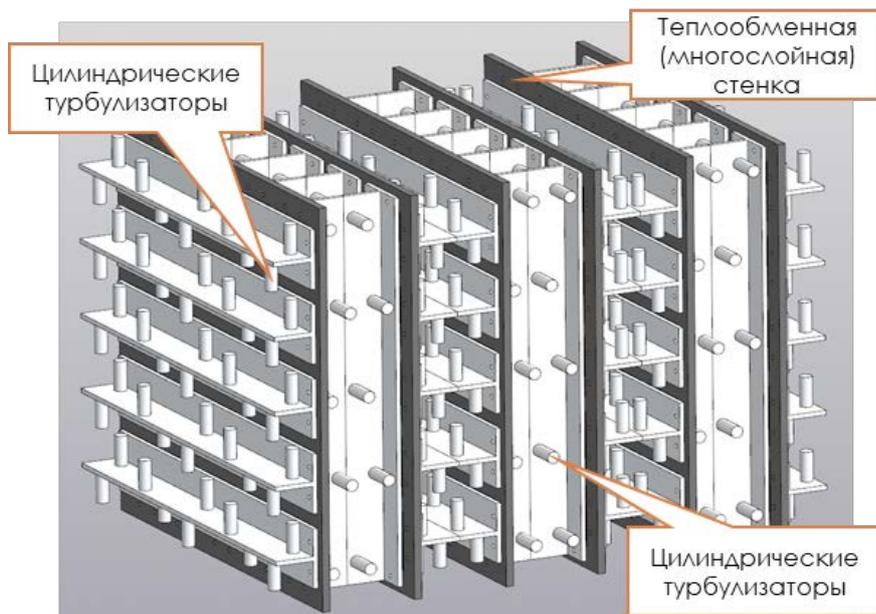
Общий вид сборки теплообменных поверхностей с шахматной схемой расположения турбулизаторов
